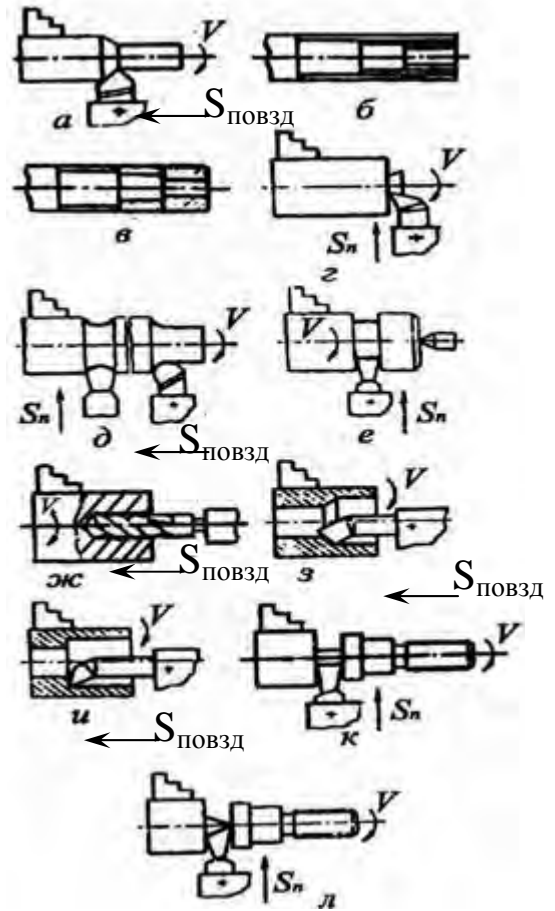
Схеми оброблення заготовок на токарно-гвинторізних верстатах
